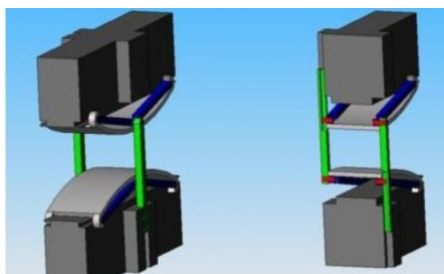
Інструмент з пружними елементами випуклої робочої поверхні [95]
